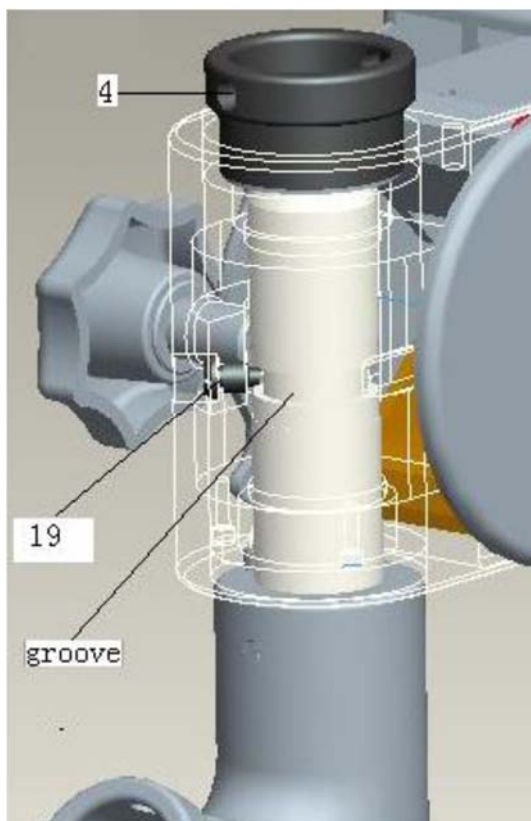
Креслення збірки з'єднувальної муфти 120°
